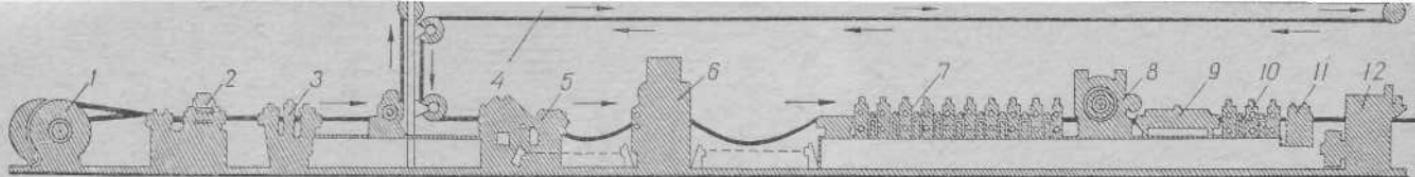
Схема расположения оборудования профилегибочного агрегата непрерывного действия:
